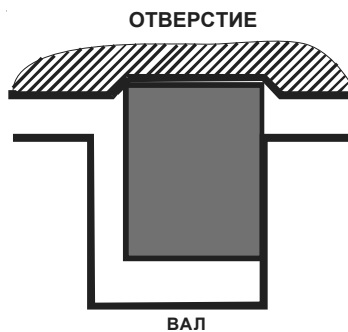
Характерный износ боковой стенки канавки, самого кольца и цилиндрической поверхности отверстия.
